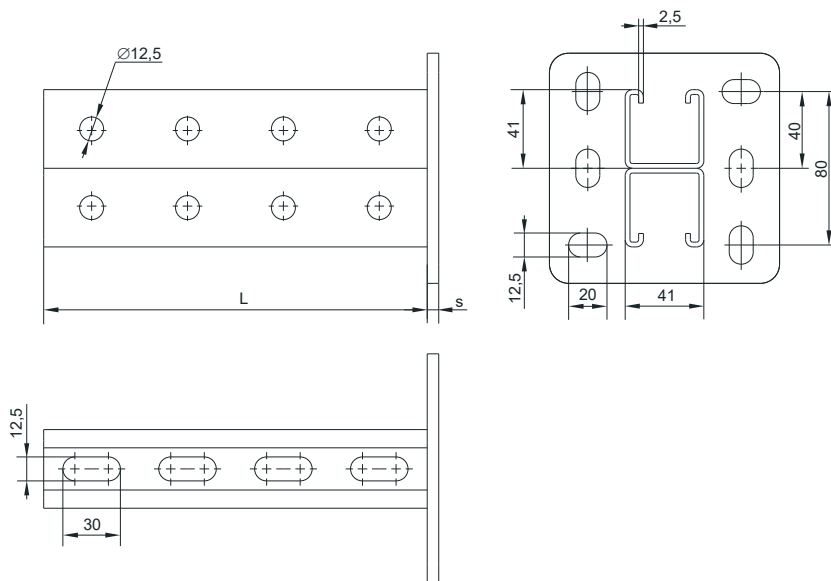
Подвес потолочный двойной 41х41 / Figure B.4 – Double ceiling suspension 41x41
